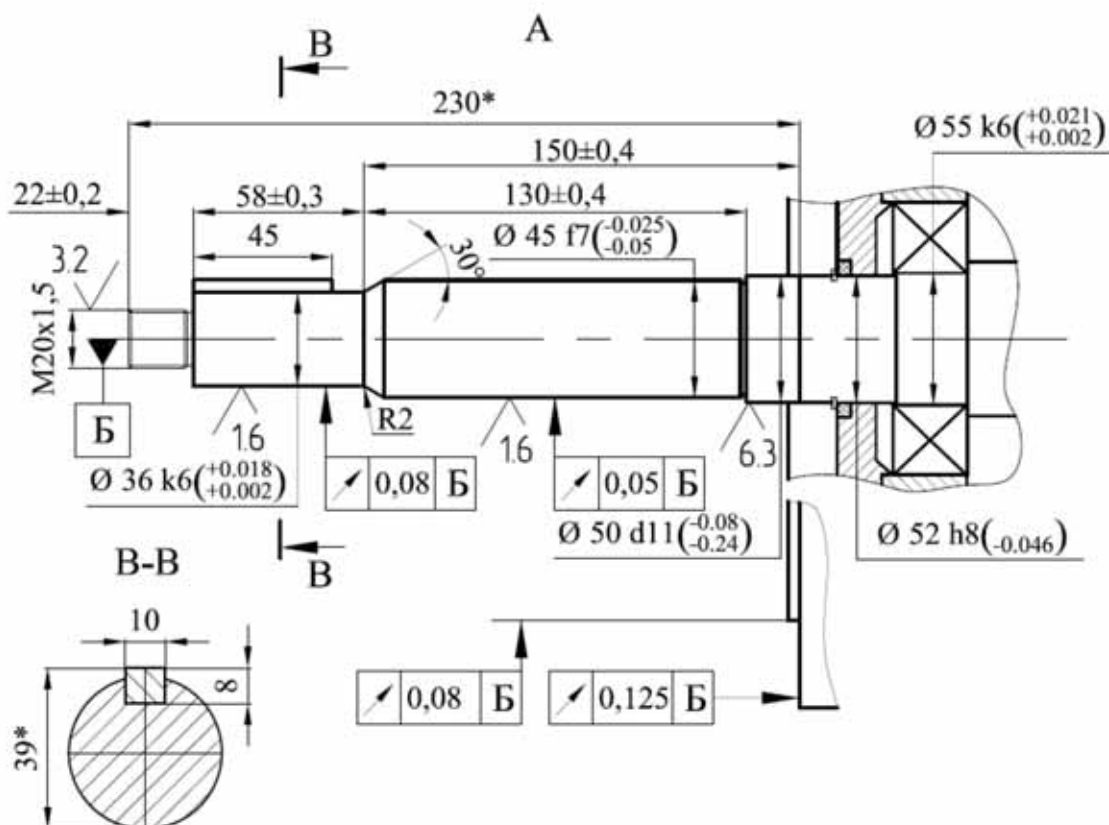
Свободный конец вала двигателя 6АМУ160М4ЖУ2, 6АМУ160М6ЖУ2
